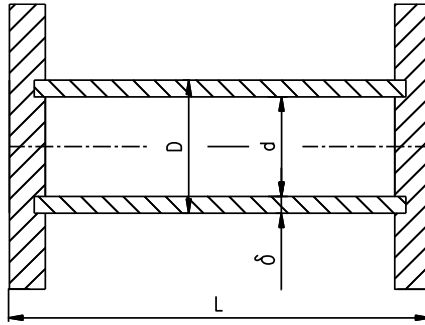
Розрахункова схема фланцевого вала.
